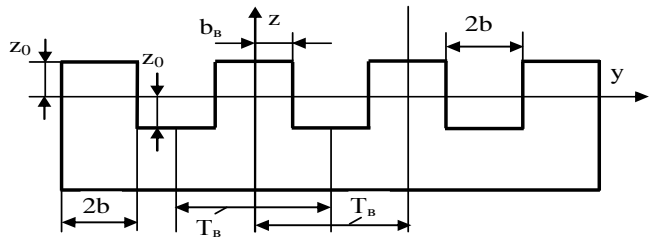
Форма сечення (x = const) заготовки з подовжними пазами
